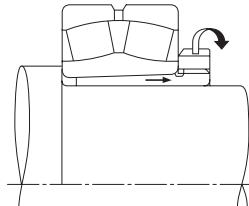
Demontage einer Abziehhülse mit Abziehmutter (1)
